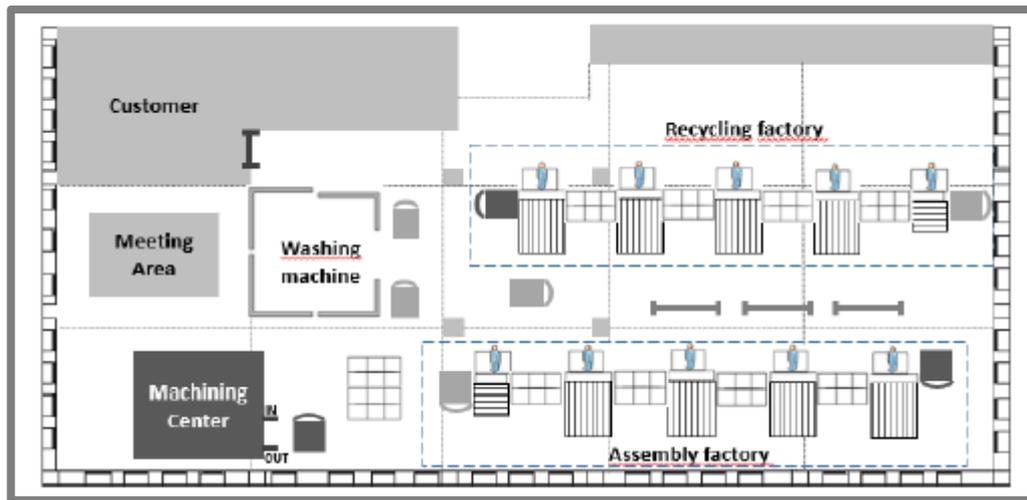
Layout de la primera producción. Fuente: Sánchez Nava, 2021
